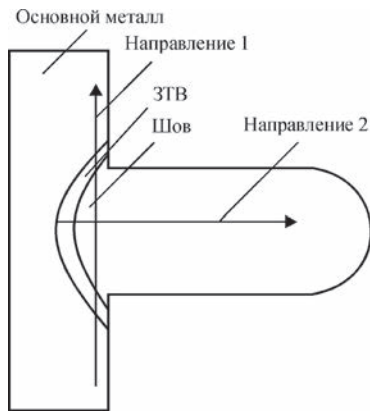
Схема измерения микротвердости наплавленного металла прямолинейной детали, изготовленной электронно-лучевой 3D-наплавкой
